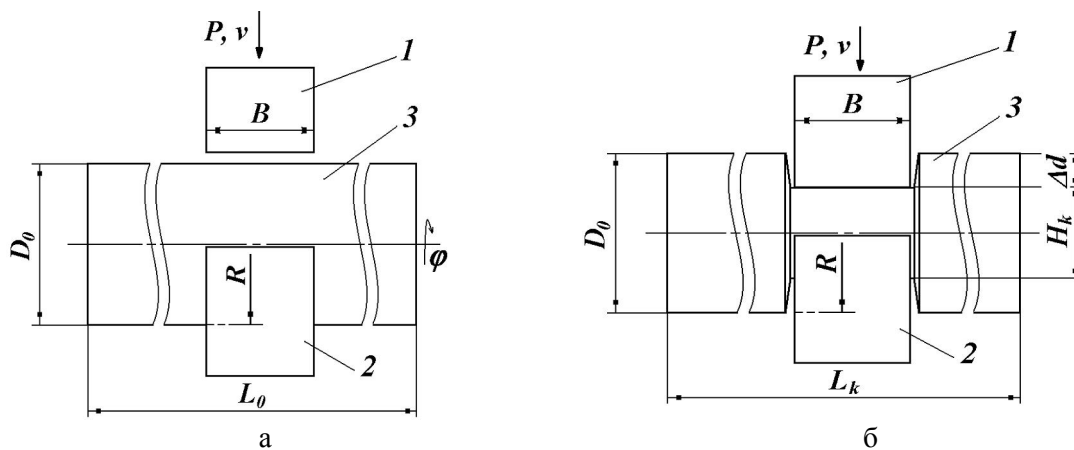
Схема протяжки заготовки до обжатия (а) и после обжатий с кантовкой заготовки (б): 1 и 2 – верхний плоский и нижний вырезной бойки, 3 – заготовка;  $P$  и  $v$  – сила при обжатии и скорость инструмента
